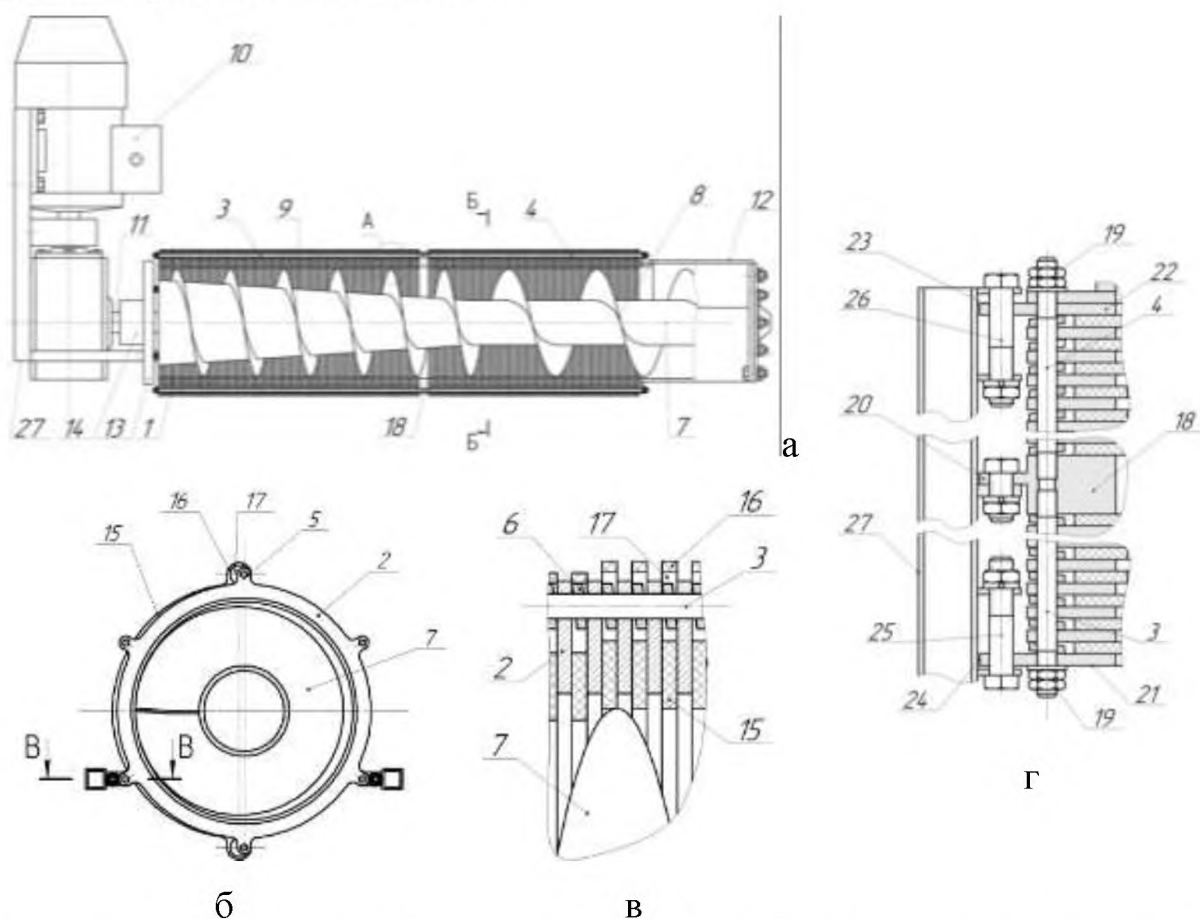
Схема преса із самоочисним фільтром: а – загальний вигляд; б – поперечний переріз; в – схема розташування кілець, г – кріплення фільтра
